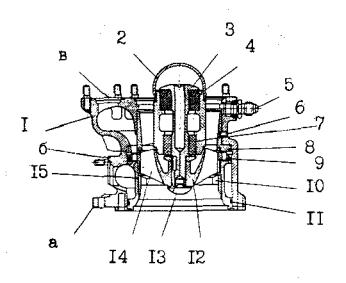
Приемный узел подвесных баков І - корпус; 2 - штуцер командного топлива: 3 - манжета; 4 - крышка; 5 - шток; 6 - пружина; 7 - сферический вкладыш; 8 - заглушка
